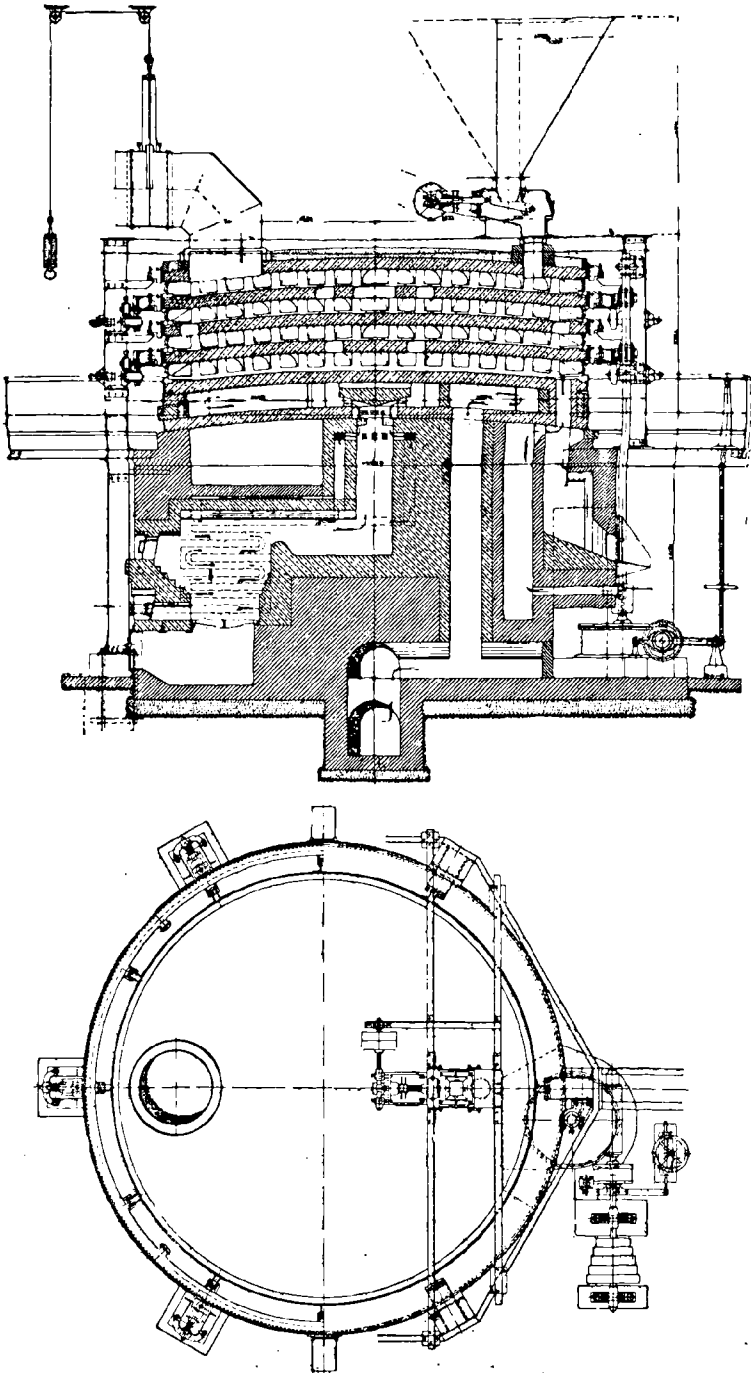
et 15. — Coupe et vue au dessus du four à Mendès De Spirlet.
